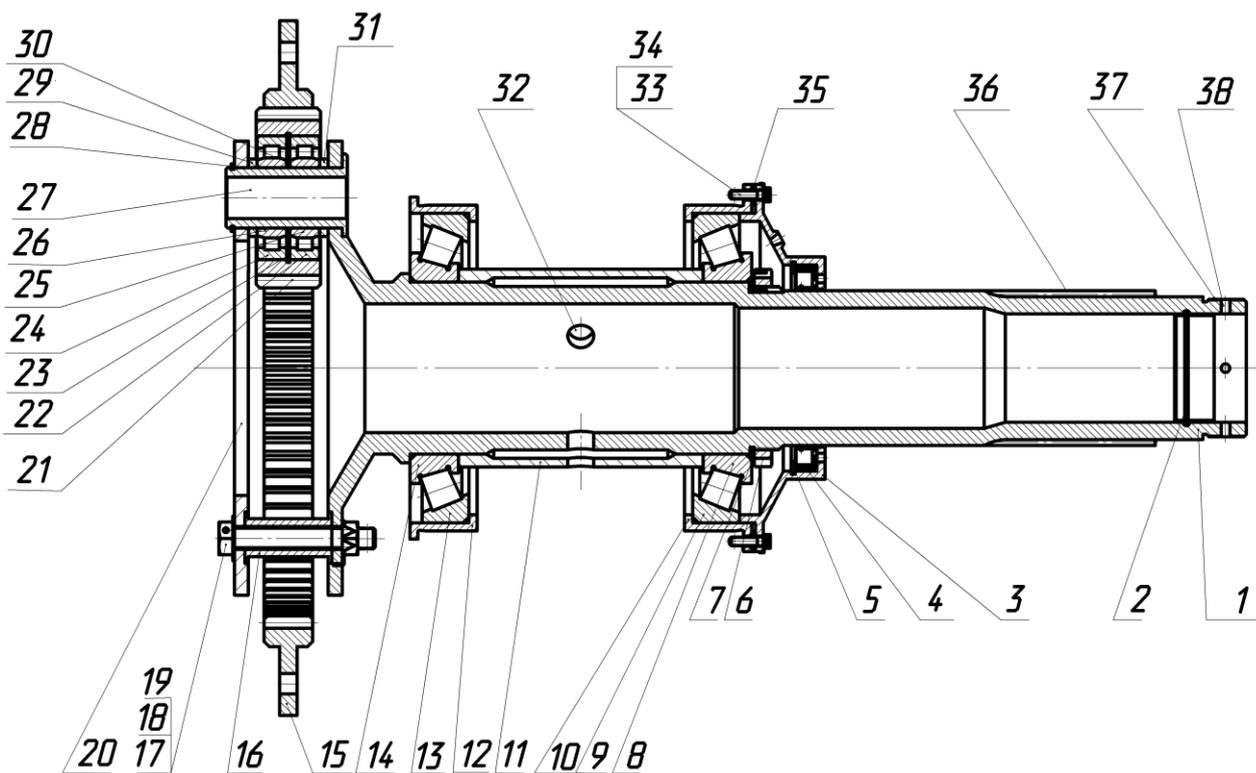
Схема сборки планетарной передачи и выходного вала
